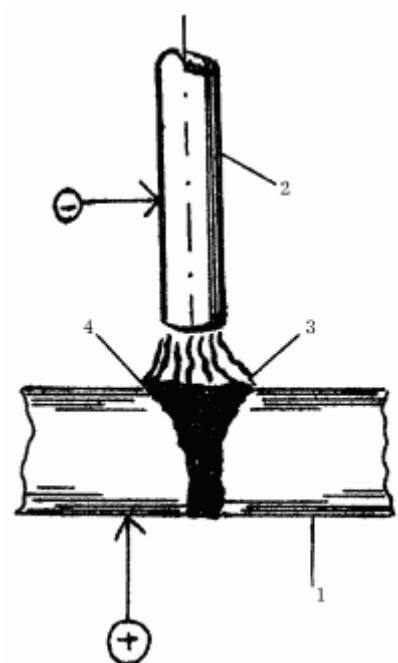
Дуговая сварка: 1 – соединяемые детали; 2 – электрод; 3 – дуга; 4 – сварочная ванна.
